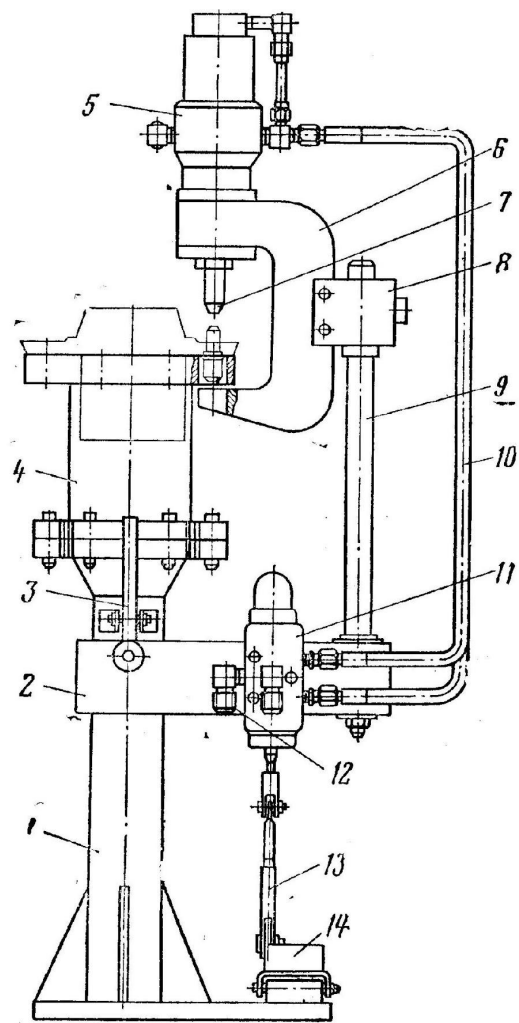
Стенд для выпрессовки шпилек из ступиц колес автомобиля
